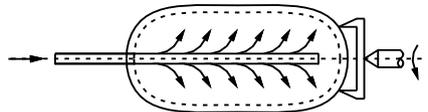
Esboço do processo de moldagem por centrifugação.
